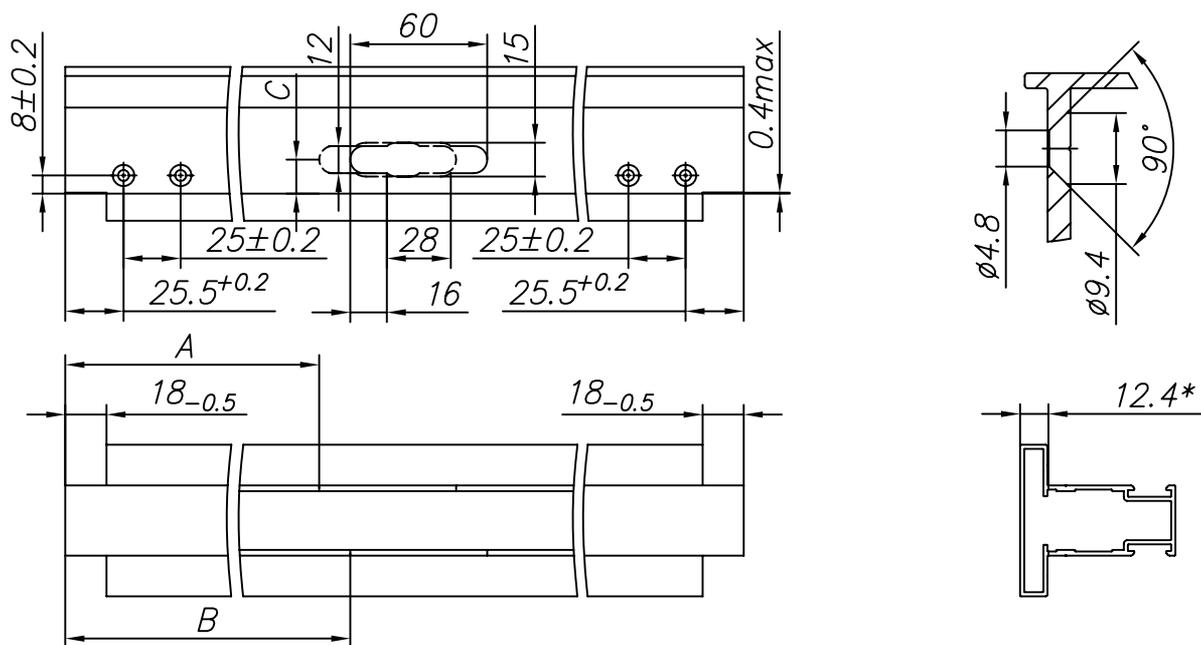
Изготовление импоста с пазами для тросовой растяжки
